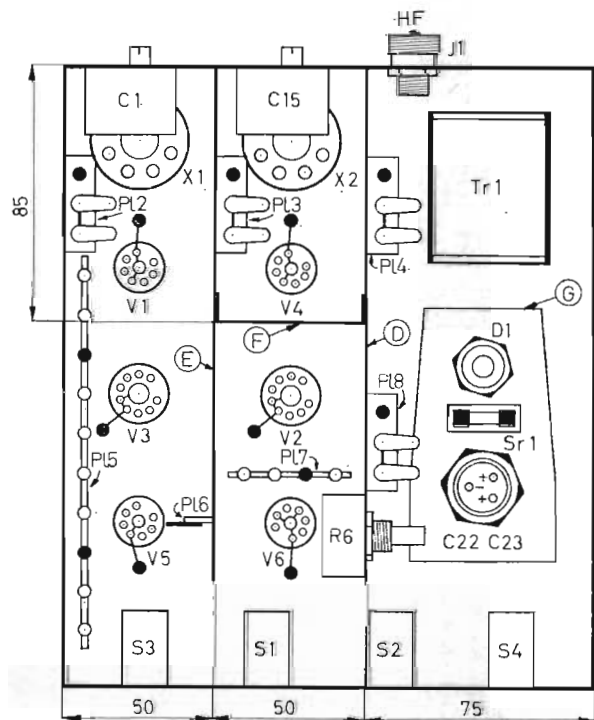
Placeringsritning för chassiet sett underifrån. Jfr fig. 13.
